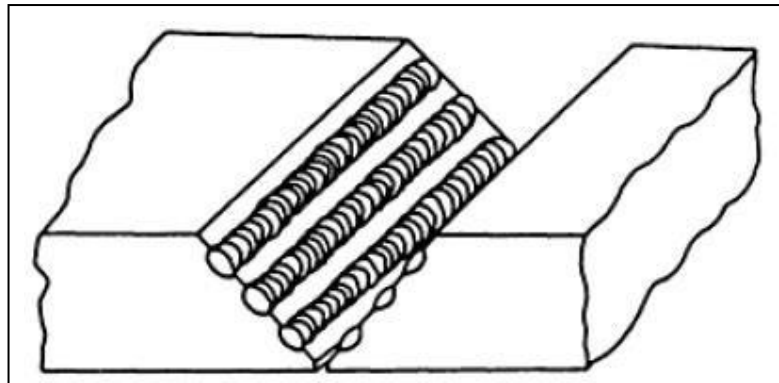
Ranuras de cordones en la junta de soldadura. [3]
